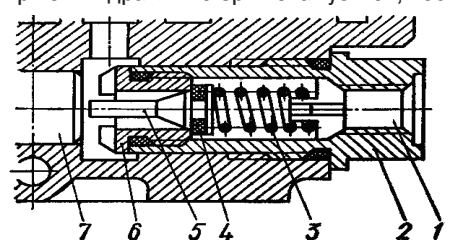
Запірний клапан секції піднімання жатки комбайнів «Нива» і «Енисей-1200»: 1 — під'єднувальний отвір; 2 — корпус клапана; 3 — пружина; 4 — гумове кільце; 5 — шток; 6 — гніздо; 7 — поршень
